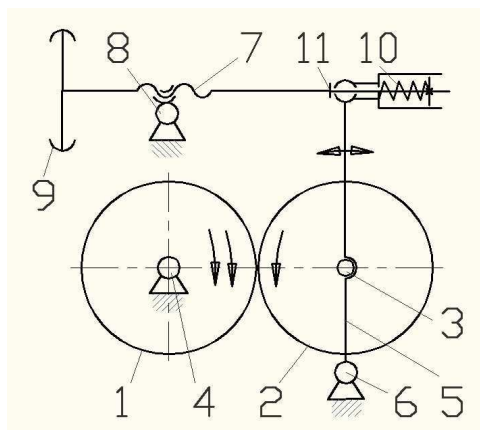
Конструкция установочного механизма с рычагами второго рода
